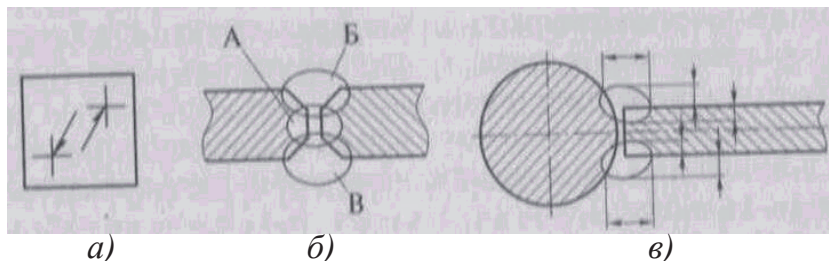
Схемы обозначения сварных швов в соединениях: а – любого стандартного; б – многопроходного; в – нестандартного
